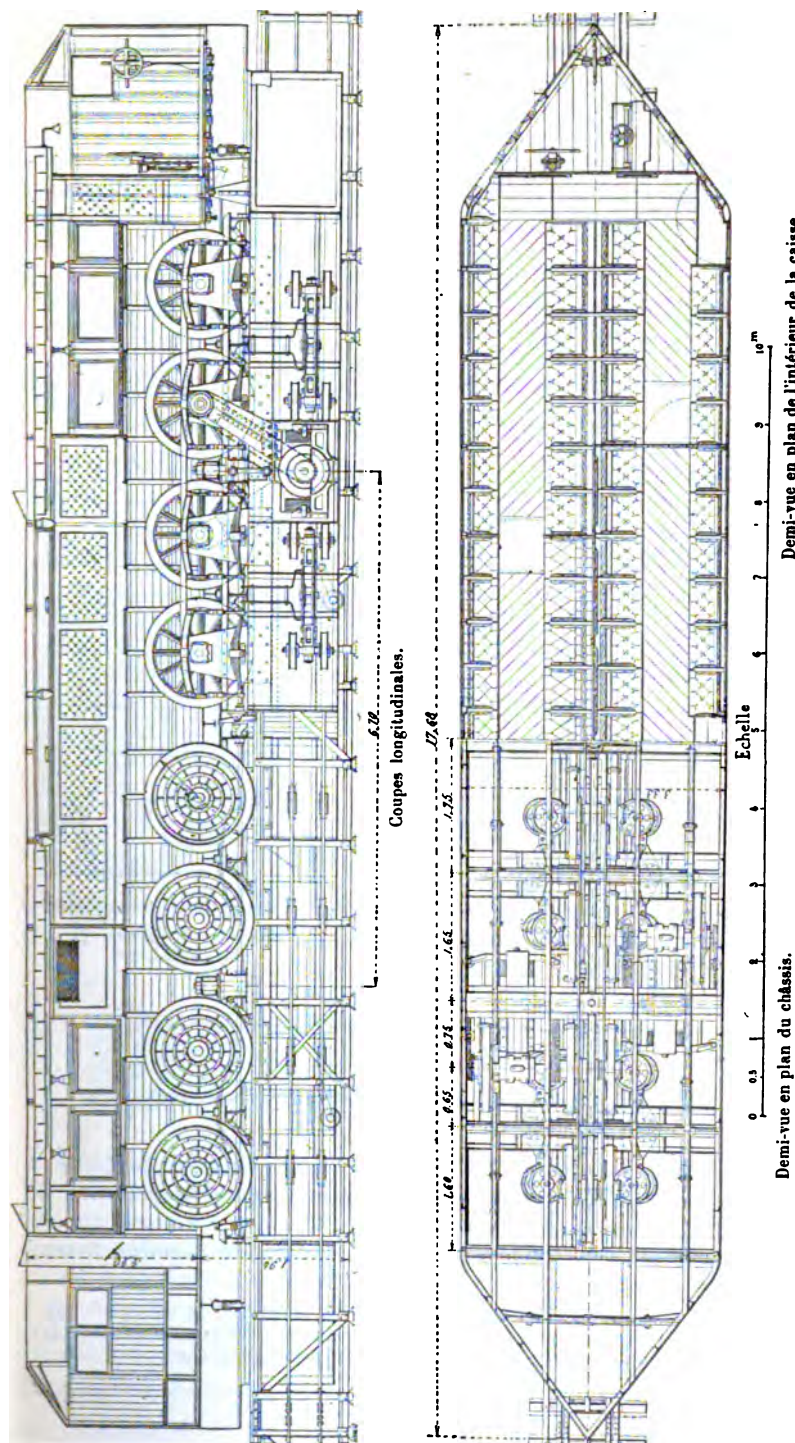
Voiture Behr. — Plan et coupes longitudinales.
